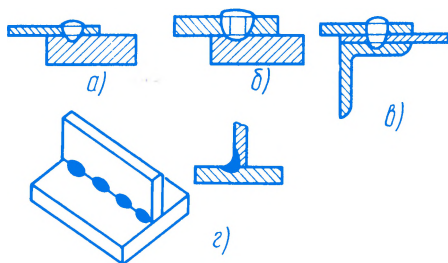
Соединения сварные точечные: а — без отверстия в верхнем листе, б — с предварительным отверстием, в — сварка двух листов с профильным элементом, г — угловое соединение
